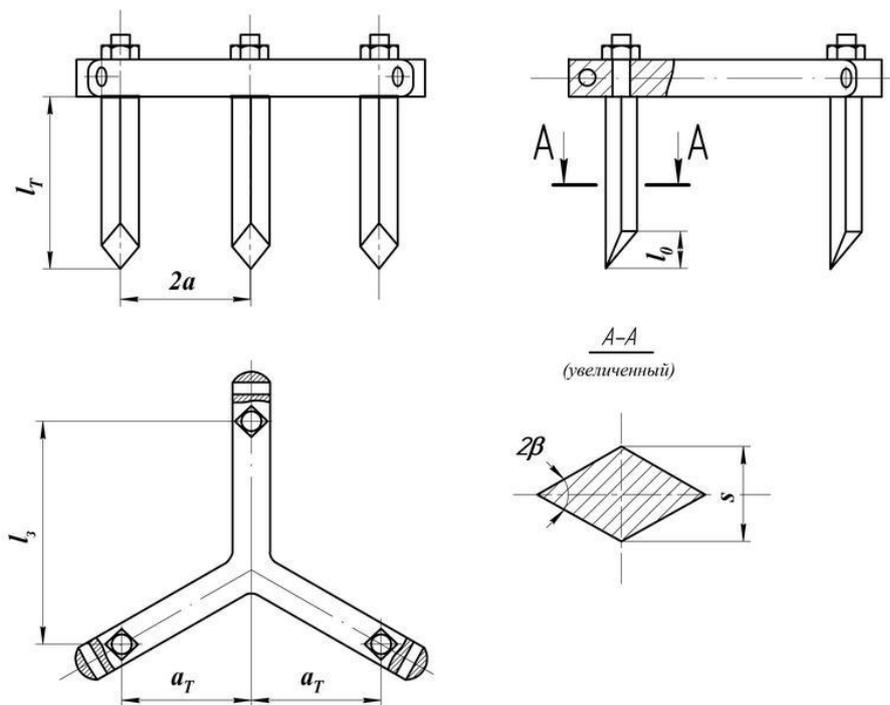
Основные параметры рабочего звена зубовой бороны, копирующей рельеф поля
